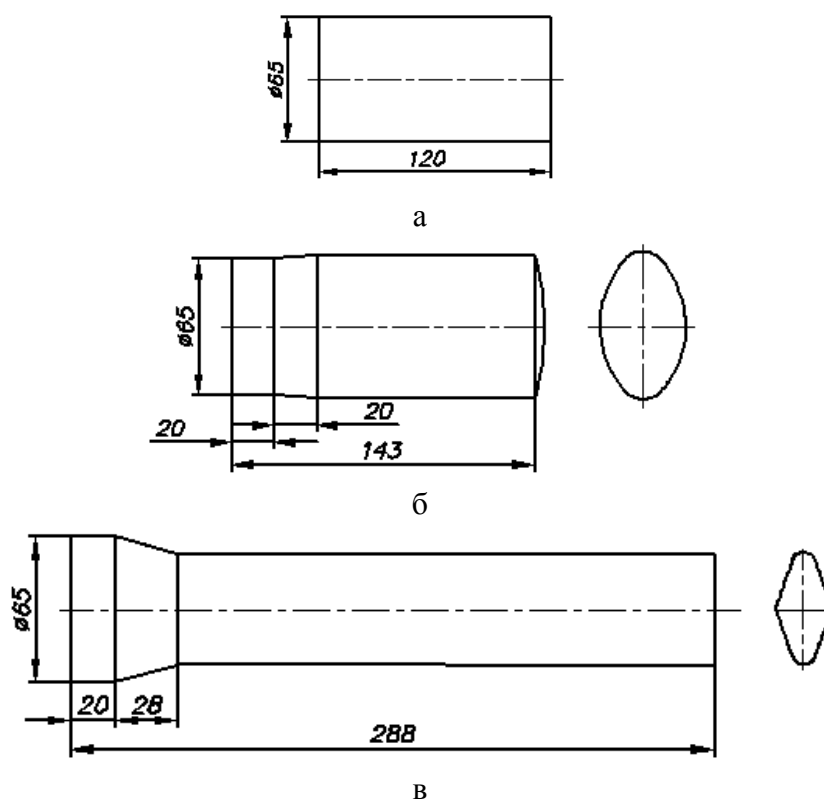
Вальцованная заготовка для штамповки поковки «фитинг»:
